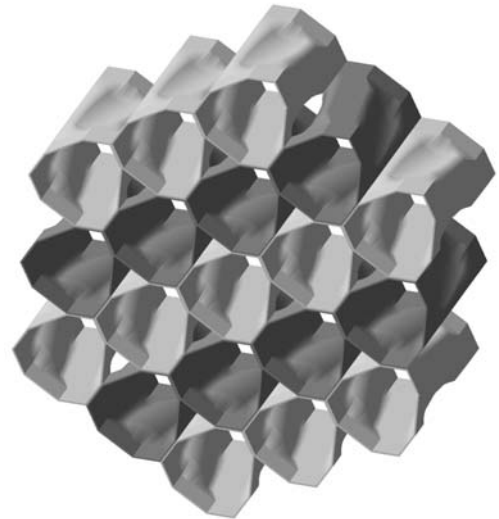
Внешний вид 19-ячеистого фрагмента сотовой перемешивающей решетки
